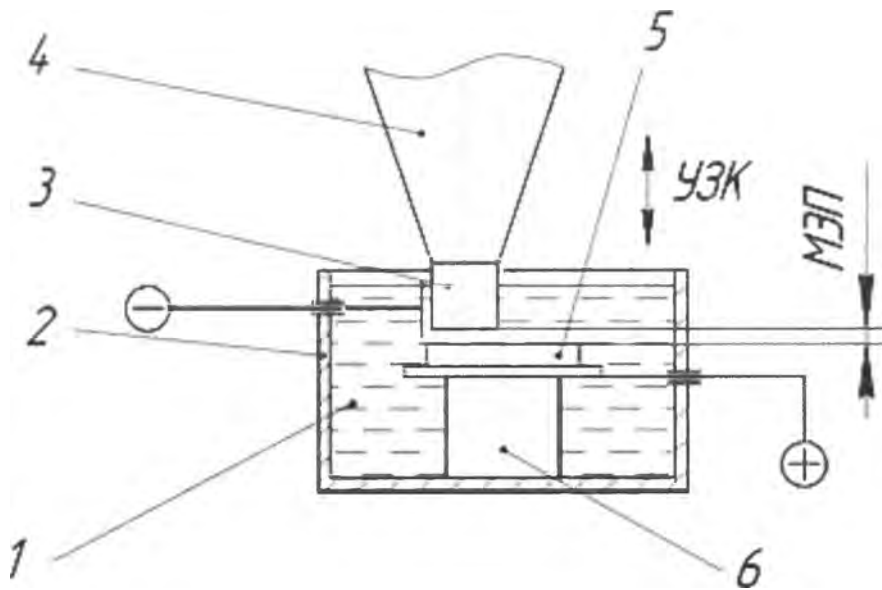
Принципиальная схема установки для электрохимической обработки модифицированной рабочей поверхности образцов
